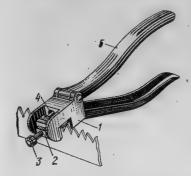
1 — гвоздодерная часть; 2 - корпус; 3 — лапа
